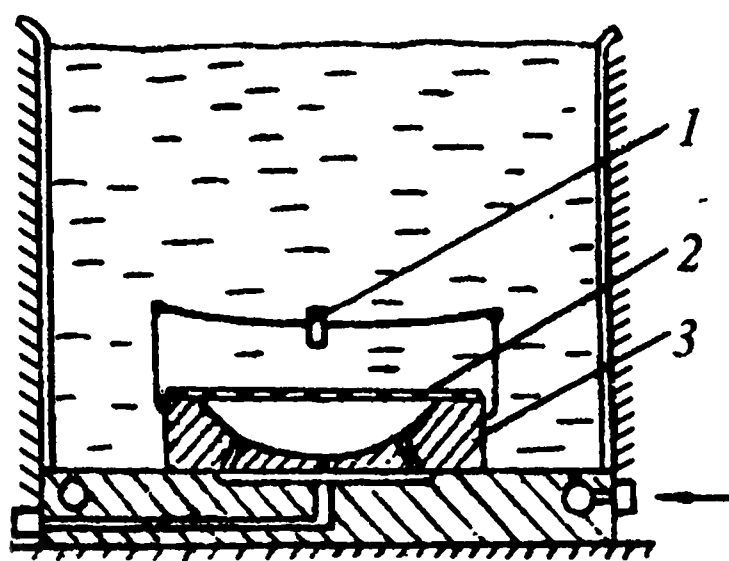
Схема штамповки взрывом: 1 — заряд; 2 — заготовка; 3 — матрица
